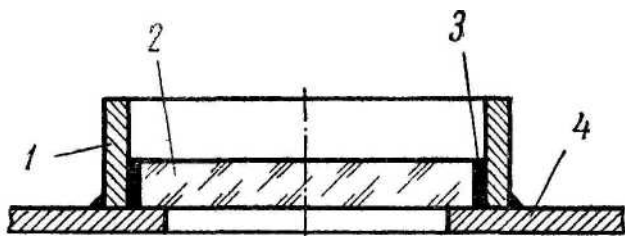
Простейший иллюминатор из плексигласа: 1 — предохранительная бленда; 2 — плексиглас; 3 — слой клея; 4 — корпус
